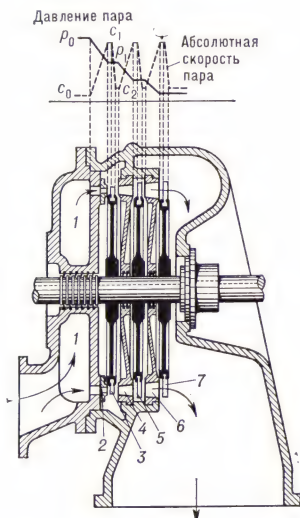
Схематический продольный разрез активной турбины с тремя ступенями давления: 1 — кольцевая камера свежего пара; 2 — сопла первой ступени; 3 — рабочие лопатки первой ступени; 4 — сопла второй ступени; 5 — рабочие лопатки второй ступени; 6 — сопла третьей ступени; 7 — рабочие лопатки третьей ступени.
